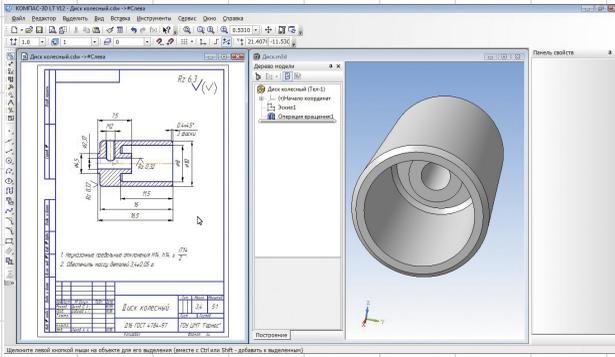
3D-модель и чертеж колесного диска для автомадели
